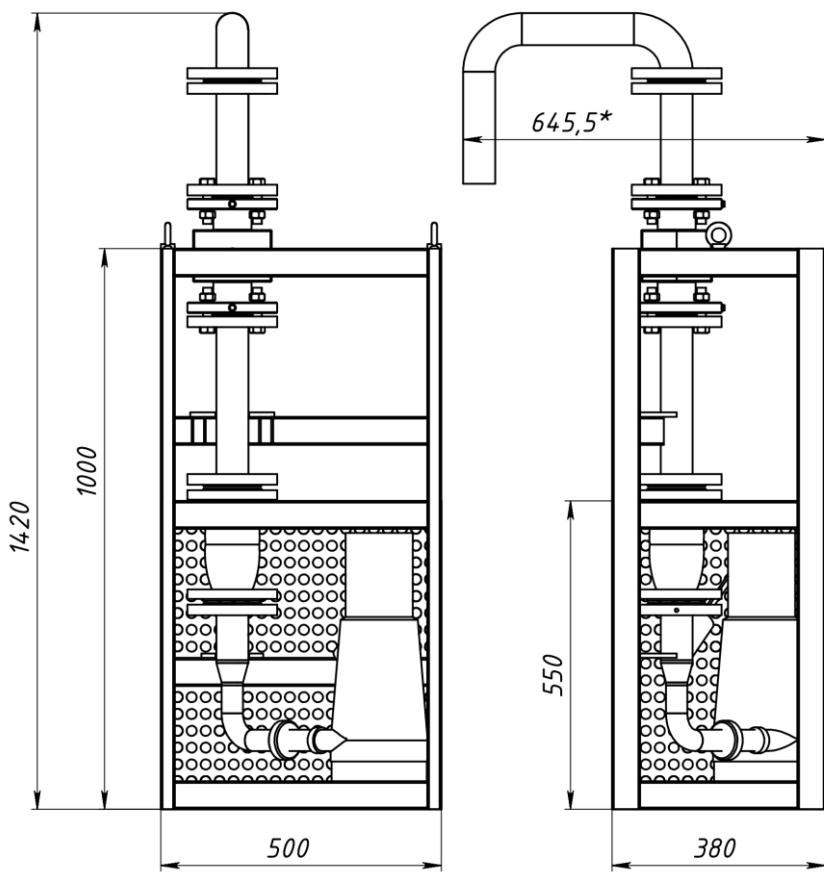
Габаритные размеры установки ТЭСМАРТ-СТОК-01
